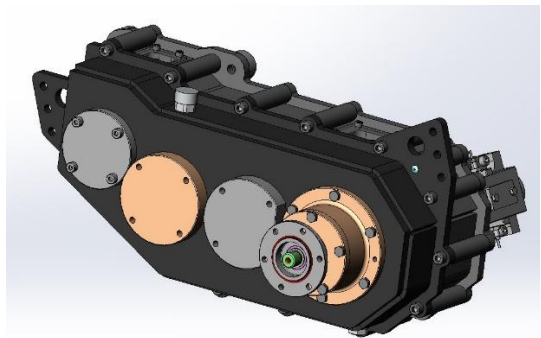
Technisches Schaubild eines Stirnrad-Getriebe (4-stufig) für elektrischen Fahrentrieb
